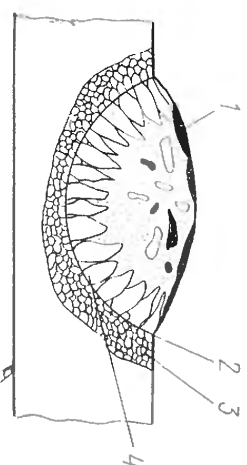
Схема кристаллизации металла в сварочной ванне.
